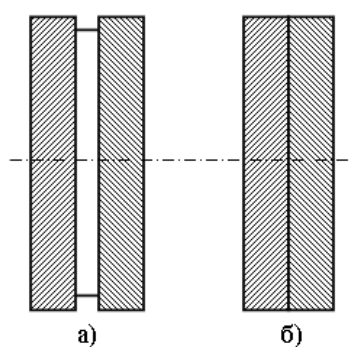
Цилиндрические зубчатые колёса шевронные
